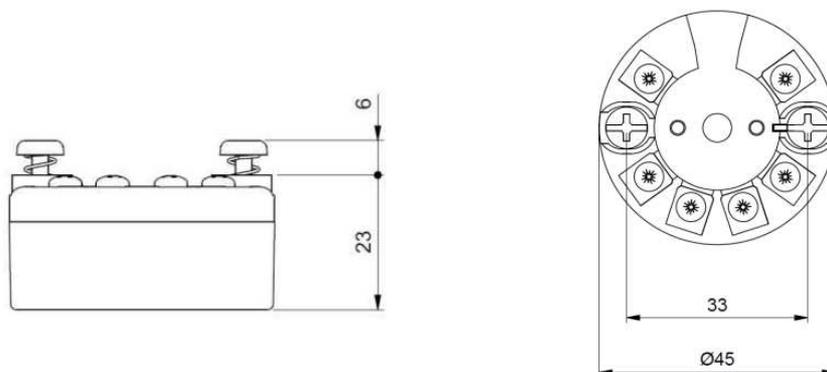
Diseño dimensional y esquema de montaje del VTT10-HP
